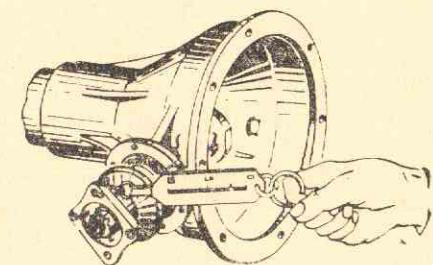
Проверка затяжки подшипников ведущей шестерни.
